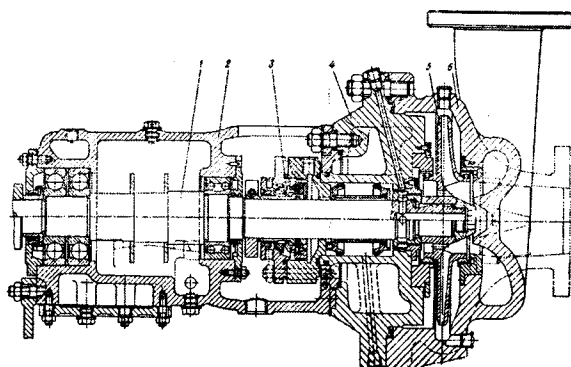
Одноступенчатый насос типа К со спиральным корпусом:
